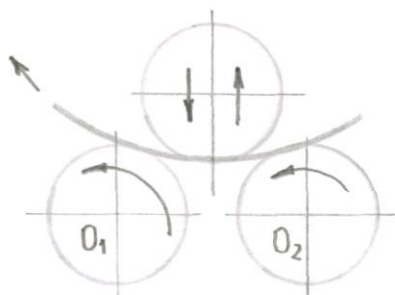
Схема гибки листовой заготовки на трехвалковой симметричной машине.
